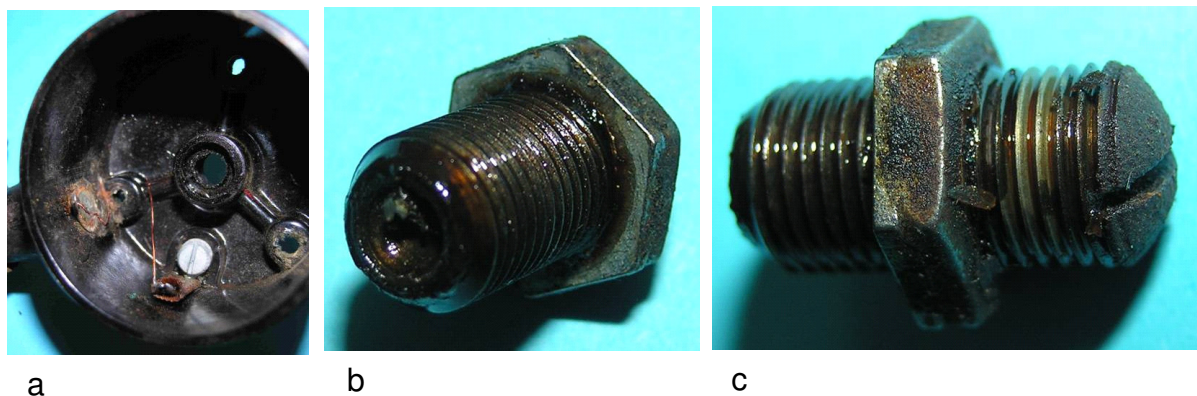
Einstellschraube des Axiallagers: a) Gehäusetopf mit zentraler Gewindebohrung, b) Sitz der Kugel, c) Schlitzschraube und Kontermutter
